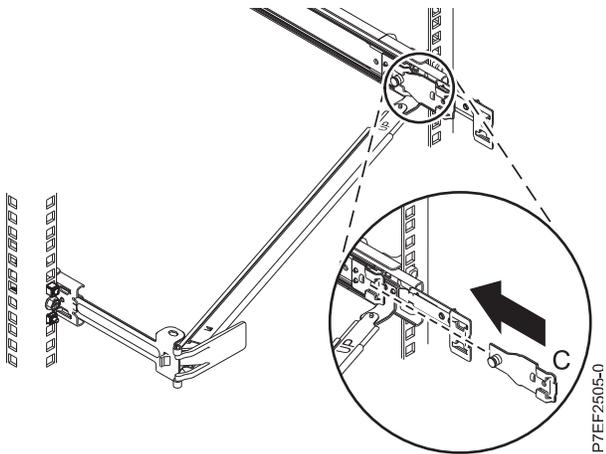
Instalación de la abrazadera de montaje en el riel deslizante
